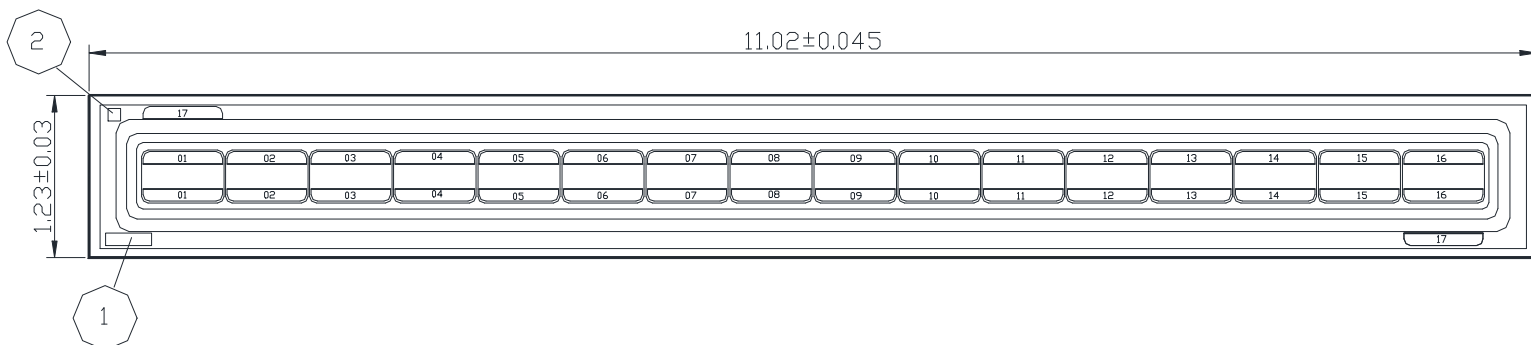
Габаритные размеры корпуса DLCC22/22-1
